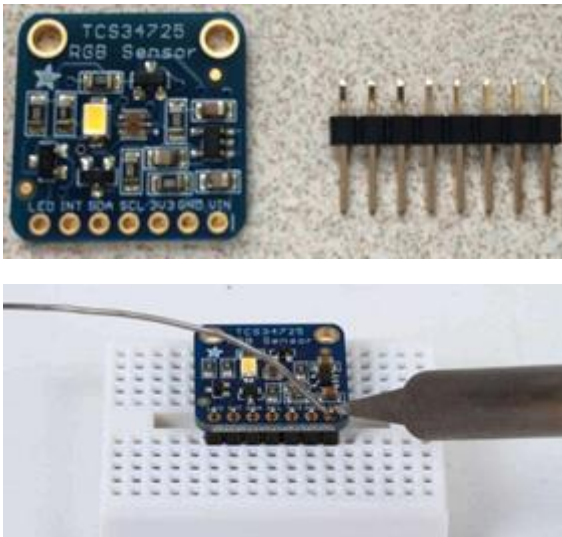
Soldar con cautín los pines machos al sensor RGB.
